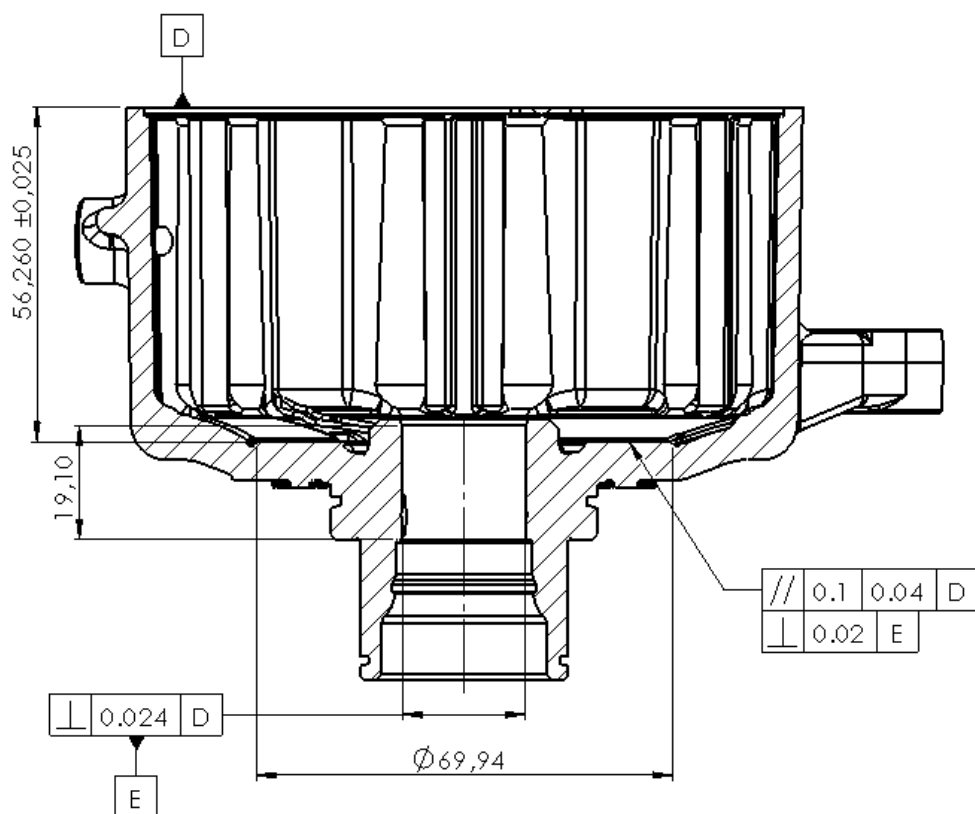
Dimensões e tolerâncias utilizadas do Cárter
